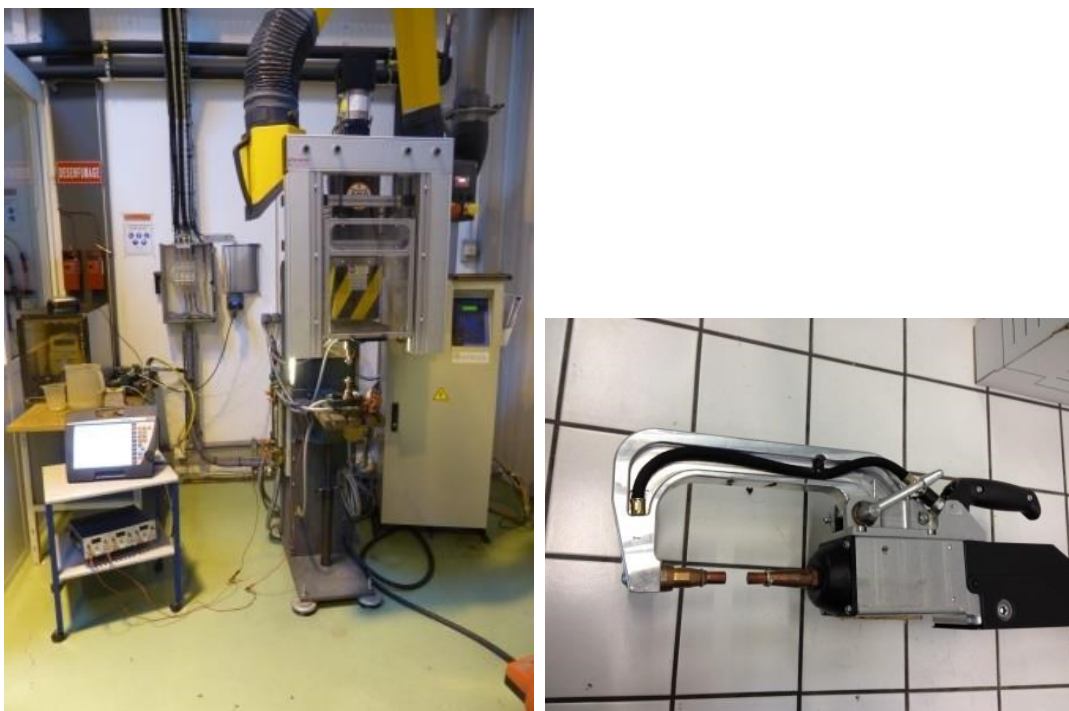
Soudeuse piédestal ARO® (gauche) et pince de soudage GYS®(droite).
